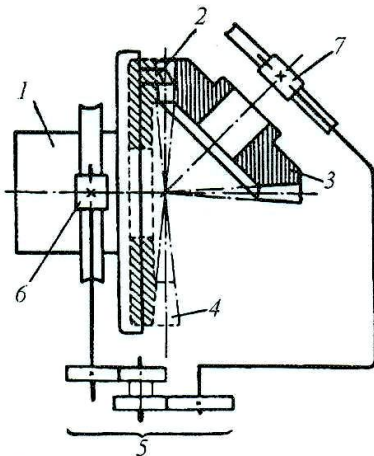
Кінематична схема верстата для нарізування зубів конічних коліс за методом обкатки
